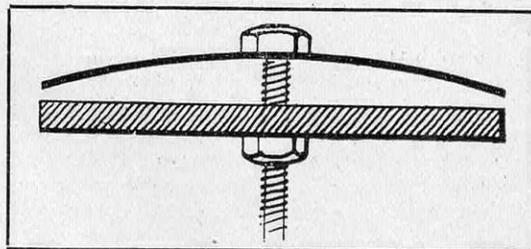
COUPE SCHÉMATIQUE DU THERMOSTAT RÉGLANT LA TEMPÉRATURE
